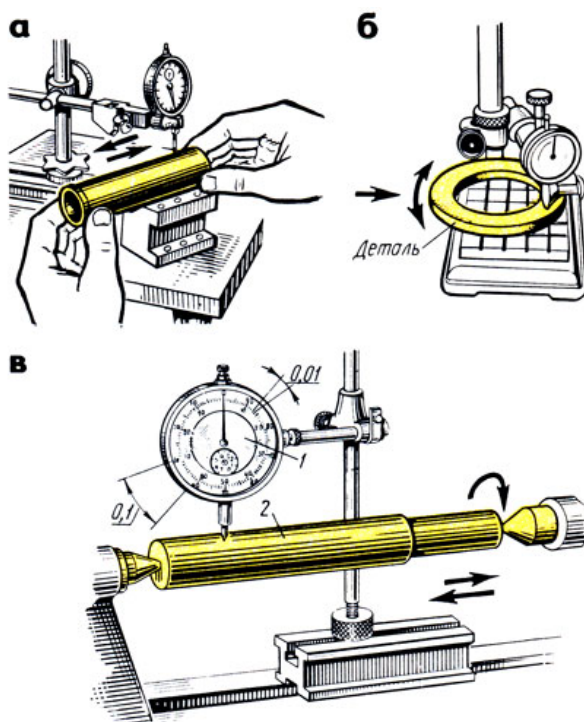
Приемы проверки индикатором: а, б - перемещением деталей, в - в центрах; 1 - индикатор, 2 - деталь
